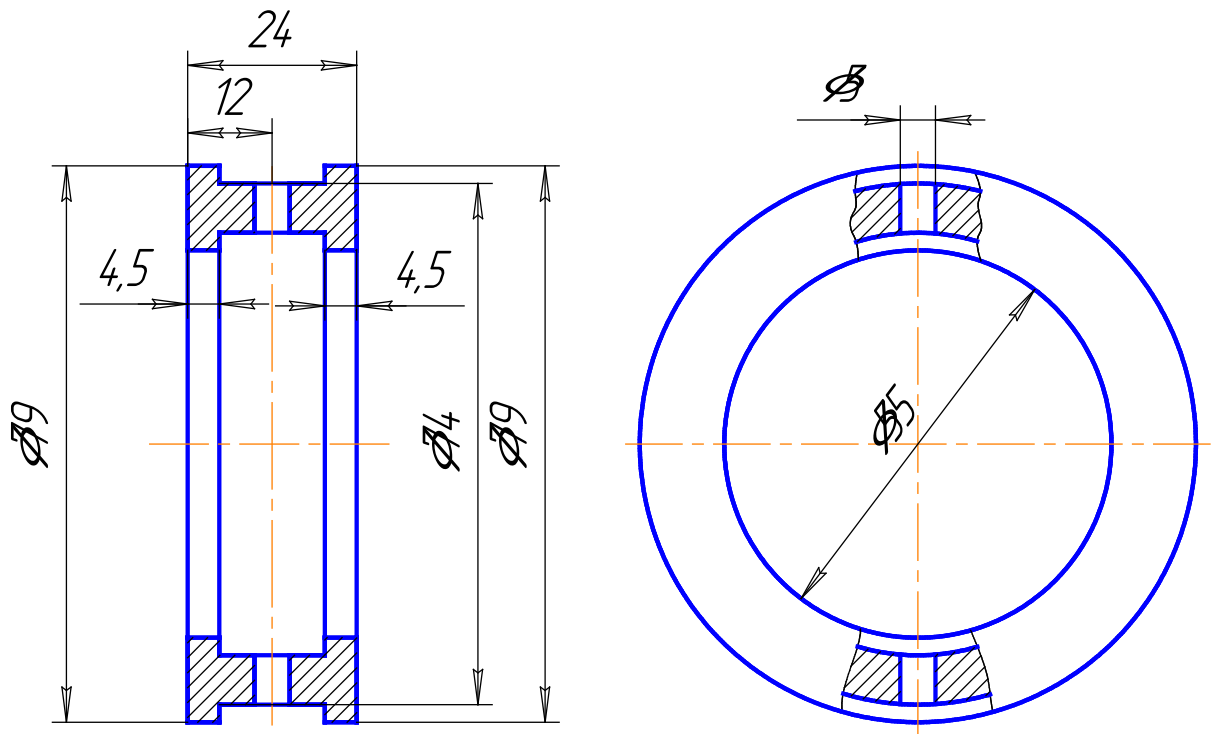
Ескіз втулки 55×24 підшипника ковзання
